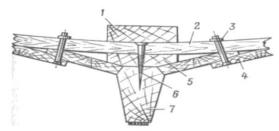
Крепление шпангоутов: 1 — кильсон; 2 — шпангоут; 3 — гвоздь с шайбой; 4 — обшивка; 5 — резен-киль; 6 — шуруп; 7 — киль
